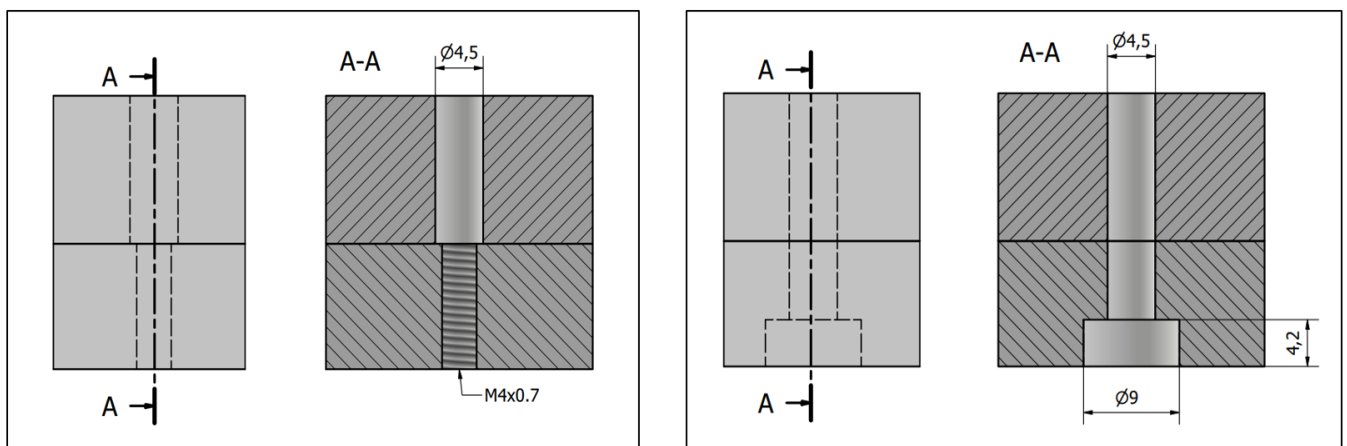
Cierre aplicado normalmente (*Izquierda*) y cierre aplicado en el molde impreso (*Derecha*).
